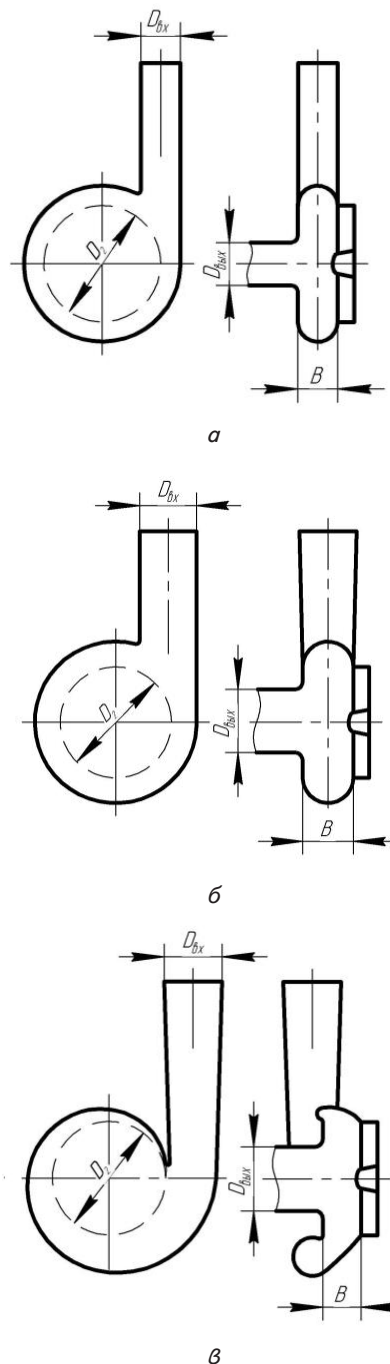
Схемы исследованных ПЧ свободновихревых насосов: а – кольцевой корпус; б – кольцевой расширенный корпус; в – корпус с несоосной спиралью
